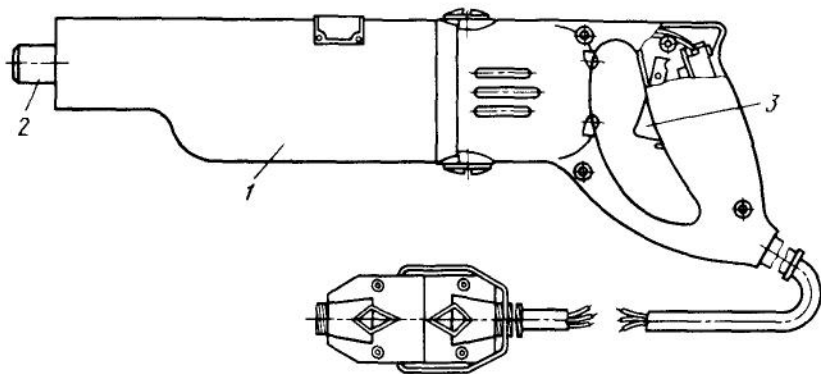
Электрическая сверлильная машина: 1 — корпус, 2 — шпиндель, 3 — выключатель
